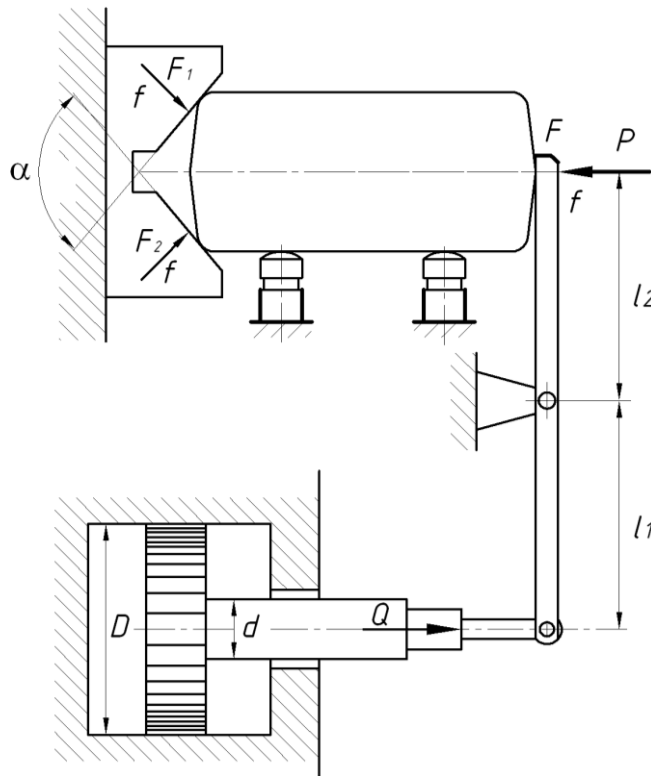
Установка заготовки при фрезерному обробленні
